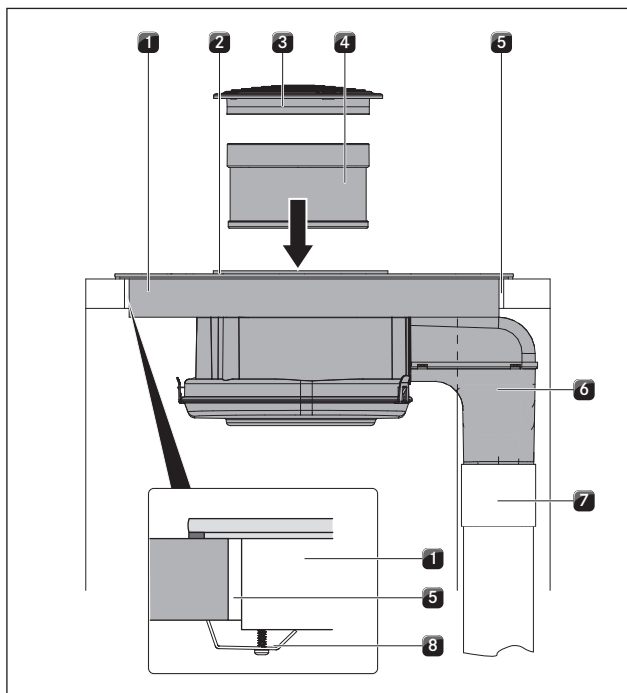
Chiudere il canale di scarico dell'aria + fissaggio
